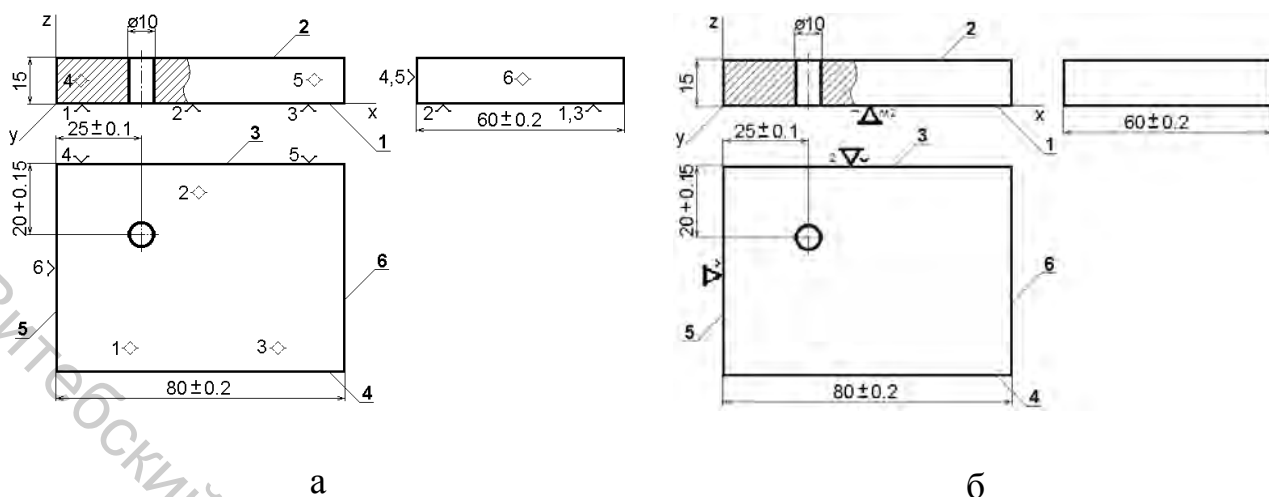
Разработка схемы базирования (а) и схемы установки (б)
